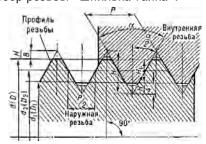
Схематическое изображение стандартного соединения «шпилька-гайка»
